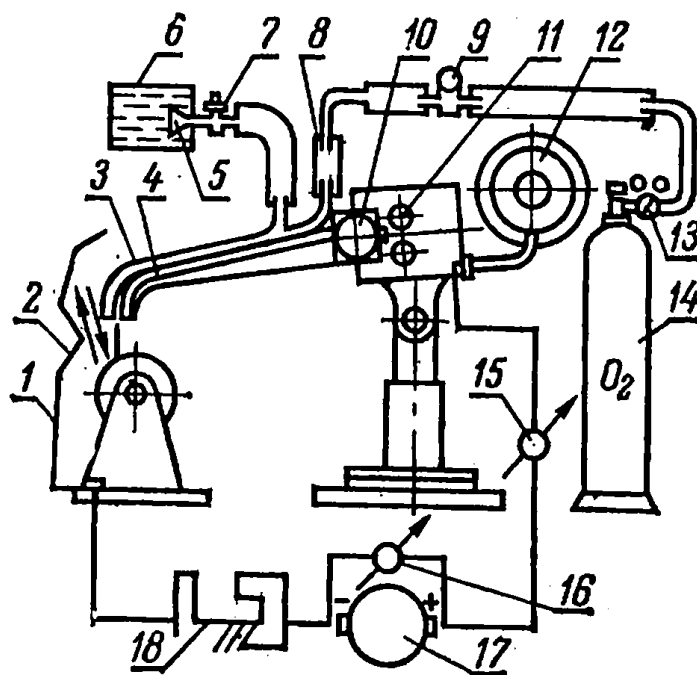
Схема установки для вибродуговой наплавки в газожидкостной среде:
